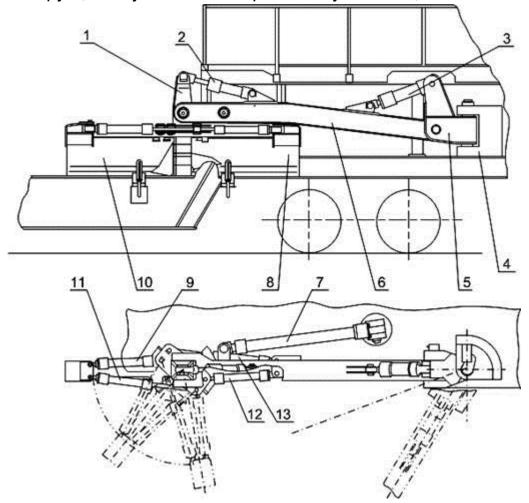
Устройство плугов: 1- подвеска; 2, 3, 7, 9, 11, 12, 13- гидроцилиндры; 4- консоль; 5- поворотный кронштейн; 6- стрела; 8, 10- крыло плуга
